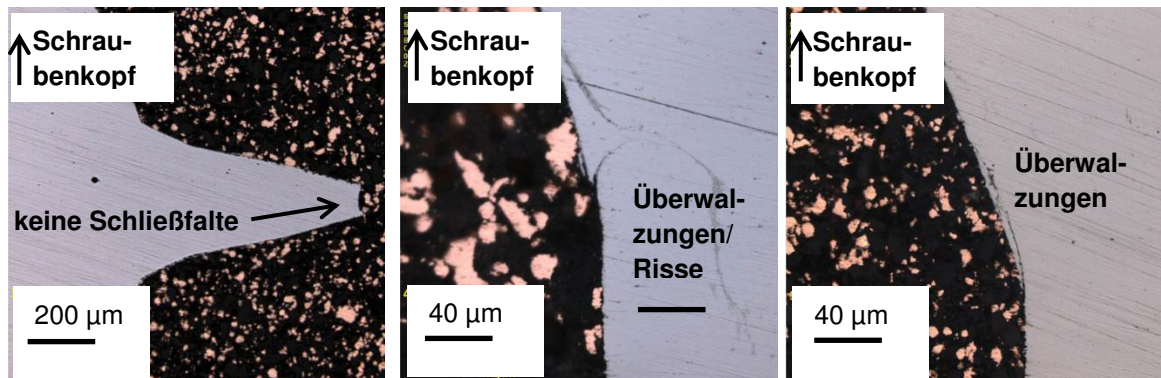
Schliffbilder bei einer zu hoch eingebauten beweglichen Walzbacke
